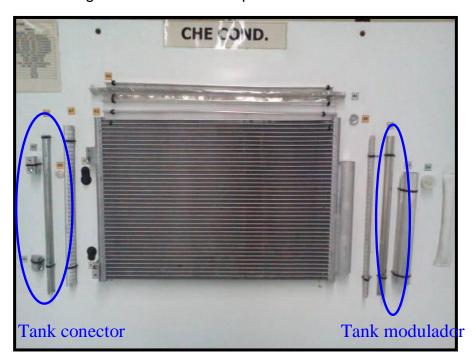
Em destaque na figura explodida do condensador CHE os tanks
